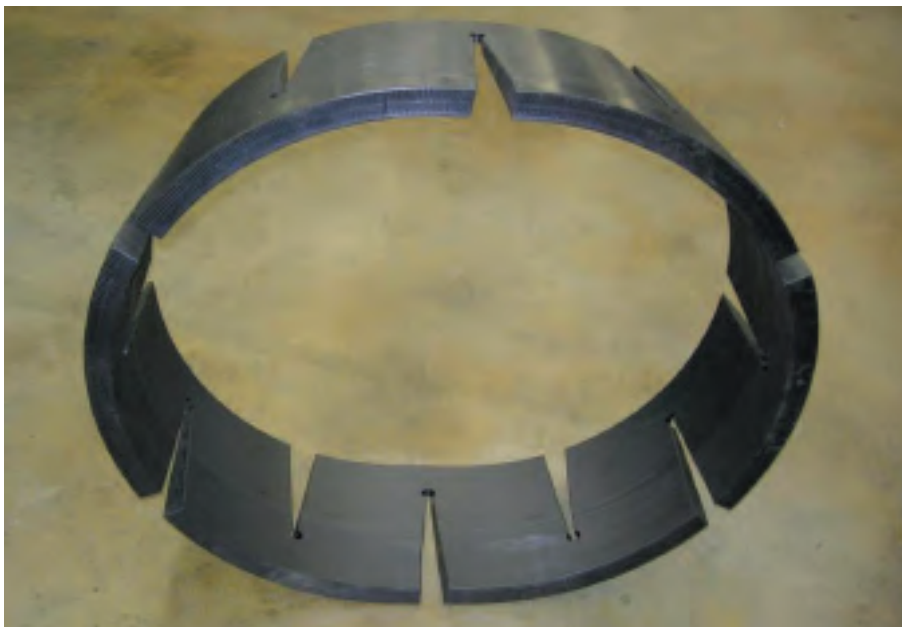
Эластичность конической сварочной втулки упрощает ее установку на трубы с большим отклонением от округлой формы
